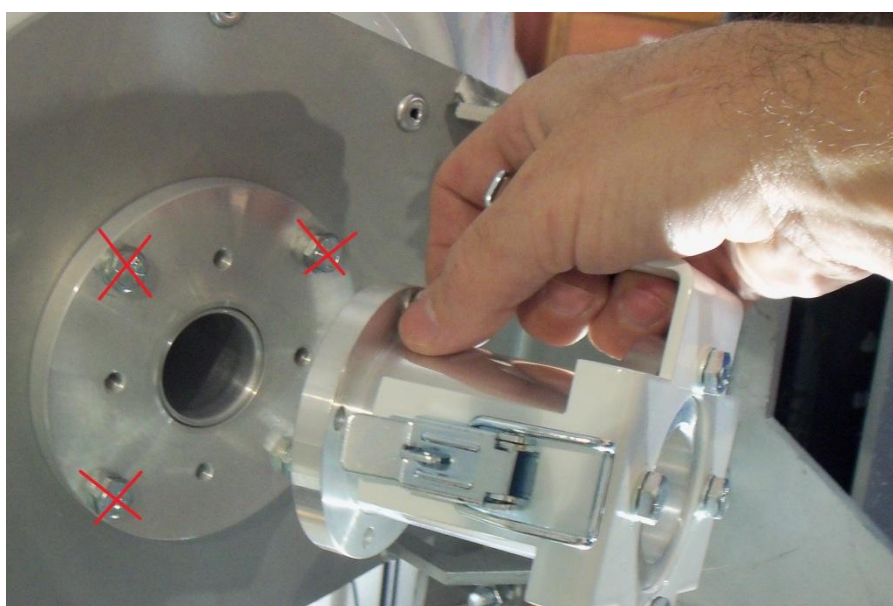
DETALHE DA FLANGE UBR84 SOLTA
